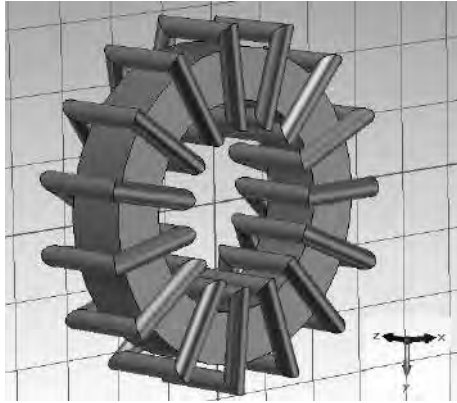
Геометрическая модель сварочного трансформатора
